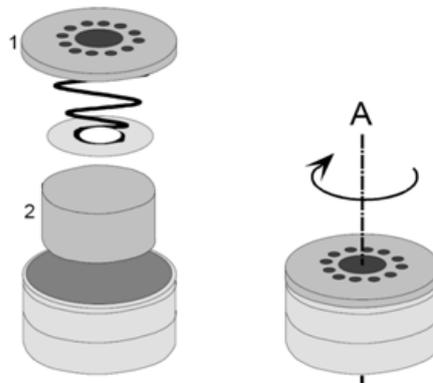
Порядок сборки кассеты: 1 – крышка, 2 – проба
